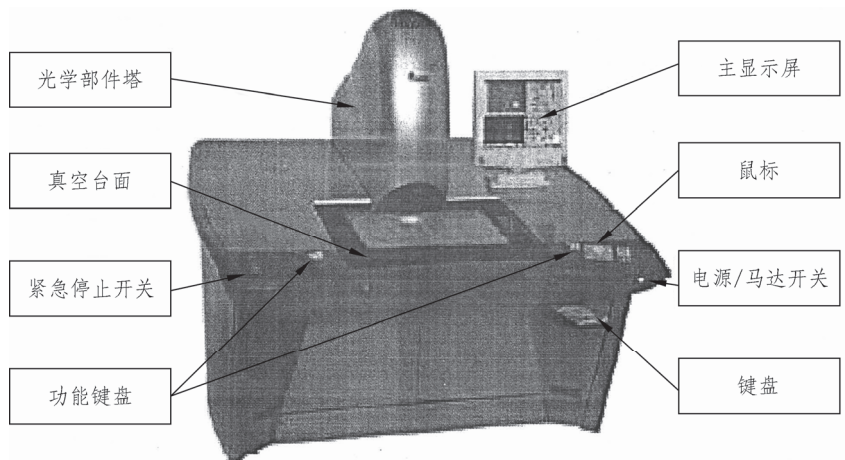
基于 AOI 的 PCB 快速智能检测设备
